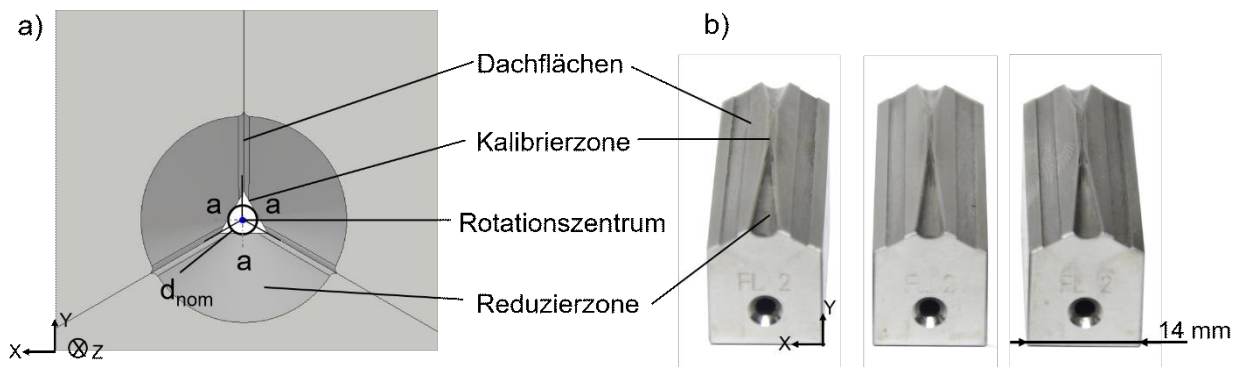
Werkzeugkonzept Flachwerkzeuge: a) Bildung eines gleichseitigen Dreiecks durch drei Flächen der FW in der Kalibrierzone; b) Werkzeugsatz bestehend aus drei Flachwerkzeugen.
